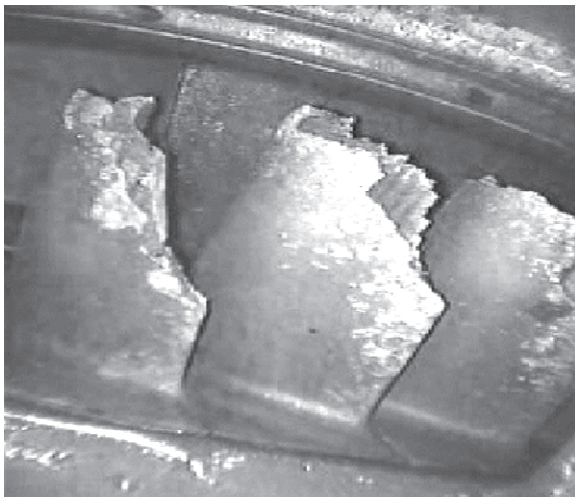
Зношені робочі лопатки осьового компресора двигуна ТВ3–117
